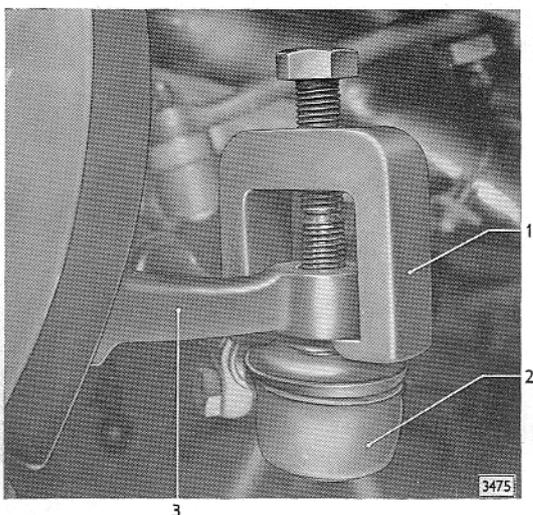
Kugelbolzen aus Lenkhebel herausdrücken
